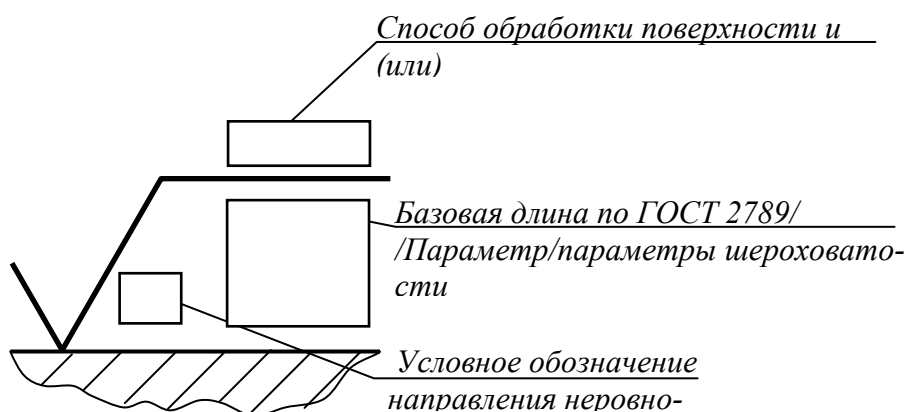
Структура условного обозначения шероховатости поверхностей на чертежах
